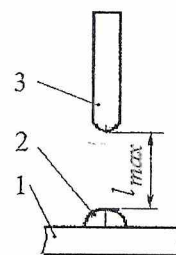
Схема замера разрывной длины дуги l_{max} : 1 – стальная пластина; 2 – наплавленный металл; 3 – электрод
